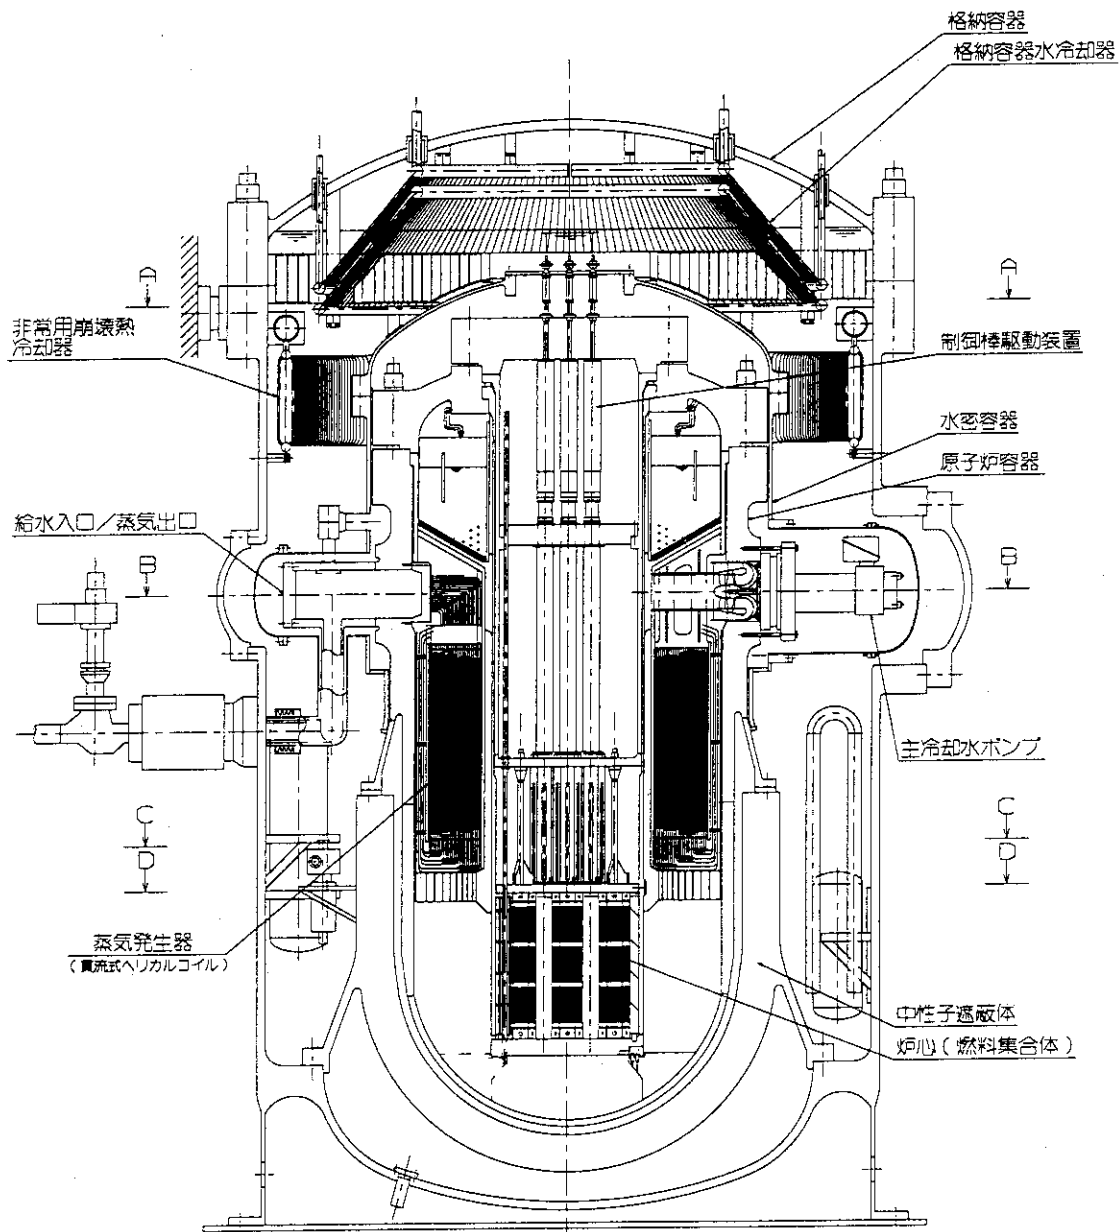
原子炉プラント全体配置図 (側面図)
